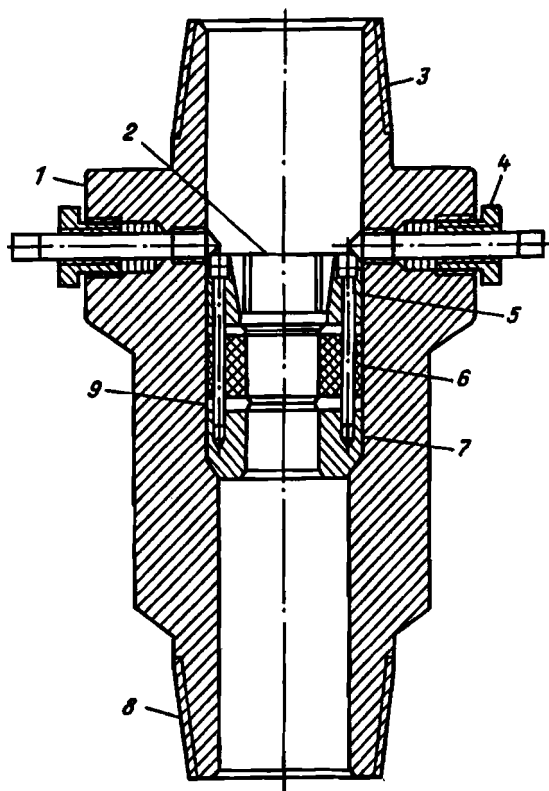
Конструкция узла подвески сифонной колонны гибких труб:
